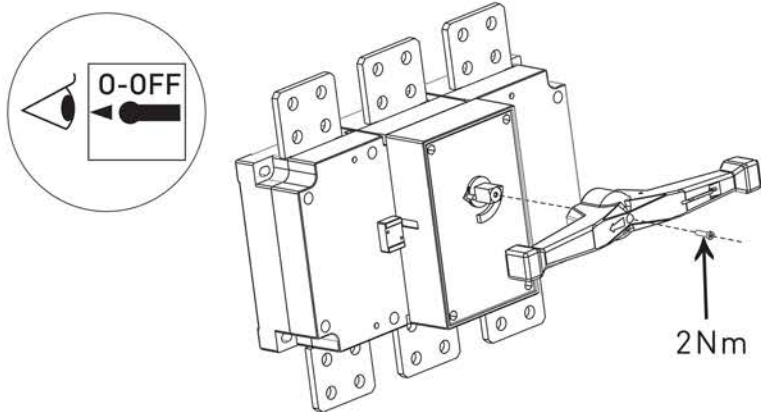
а – Монтаж ручки на корпус рубильников 1000-1600 А
